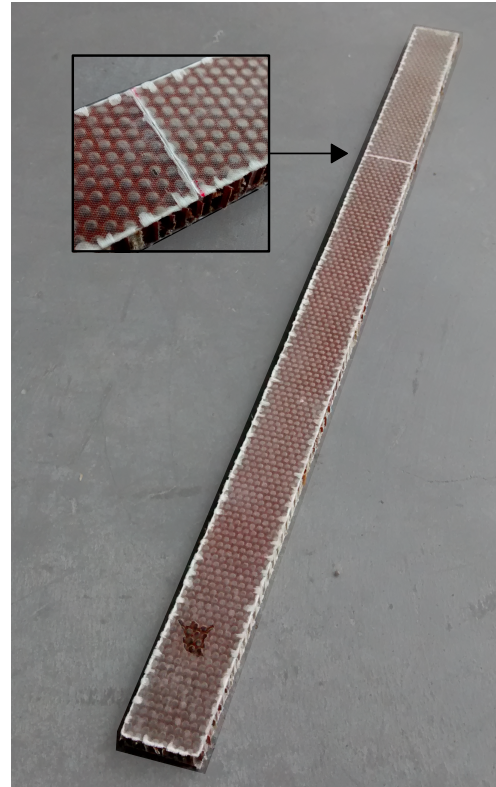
Poutre composite multicouche présentant un défaut de rupture de fibres.
